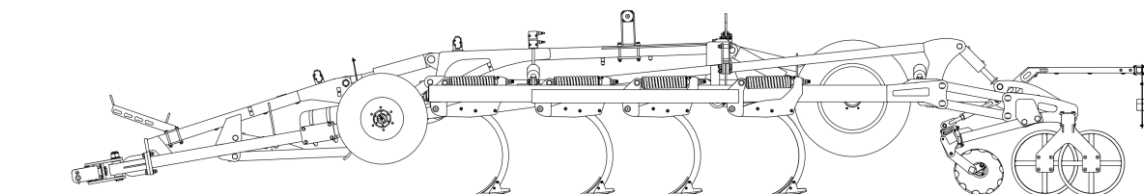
Positionnement incorrect de la machine (exemple : roue de jauge inégalement abaissée par rapport aux ensembles de rouleaux)
